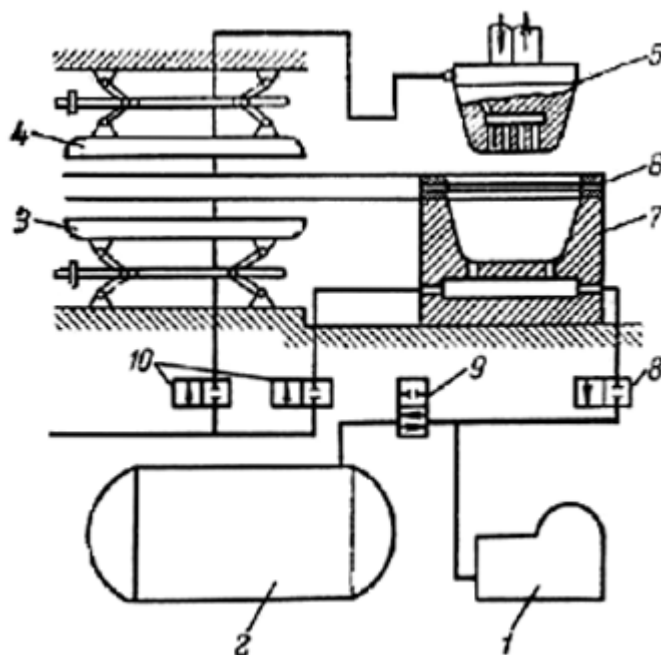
Схема однопозиційної машини для пневмо-вакуум-формувань: 1 – вакуум-помпа; 2 – ресивер; 3, 4 – нагрівачі; 5 – верхній пуансон; 6 – рамка; 7 – форма; 8, 9 – клапани; 10 – клапанний розподільник.
